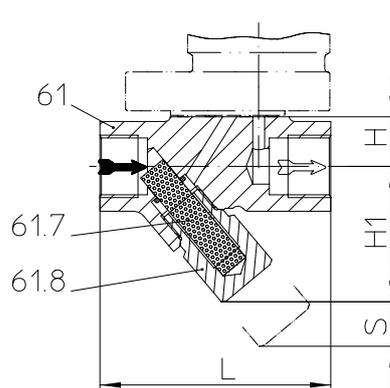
2 mit außenliegendem Sieb und Gewindemuffen
